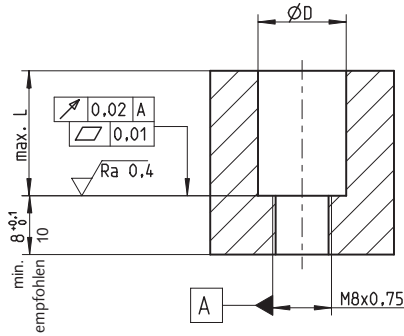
Einbau brennraumbündig. Bohrung  $\varnothing$  gemäß Werkzeug Bild 5 oder Bild 6
